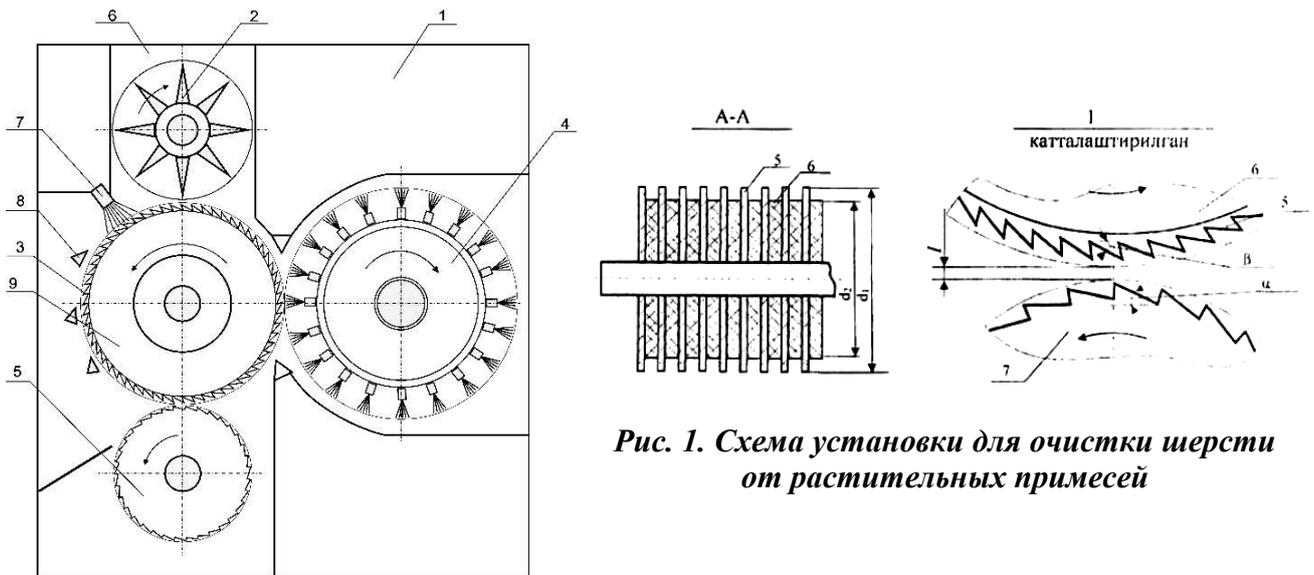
Схема установки для очистки шерсти от растительных примесей
